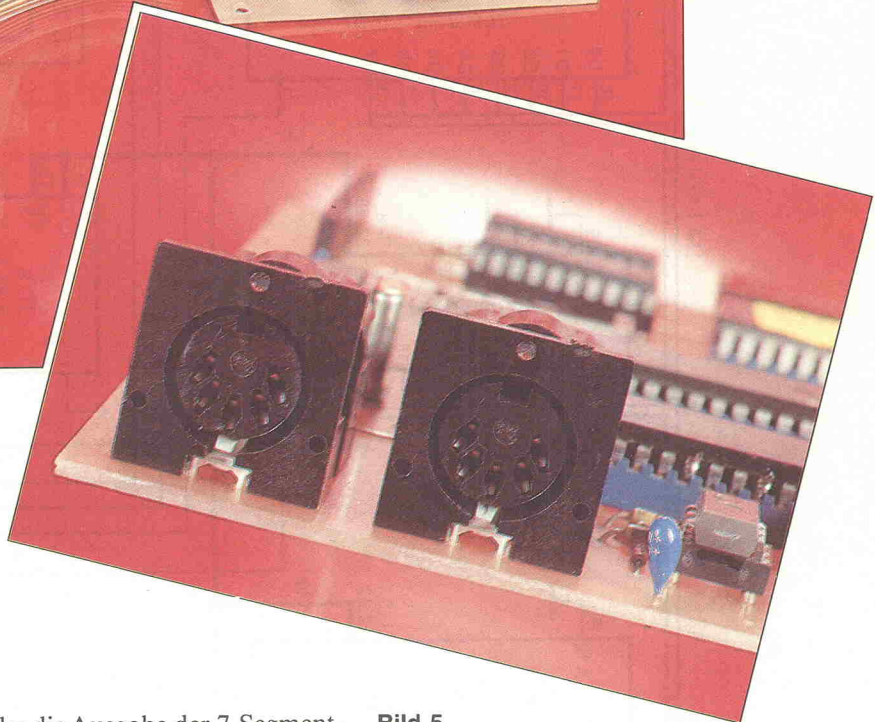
Die DIN-Buchsen für MIDI-IN und -OUT (Kontaktradius 180°) können auch in der Flanschfassung gekauft und an der Geräterückwand befestigt werden.
